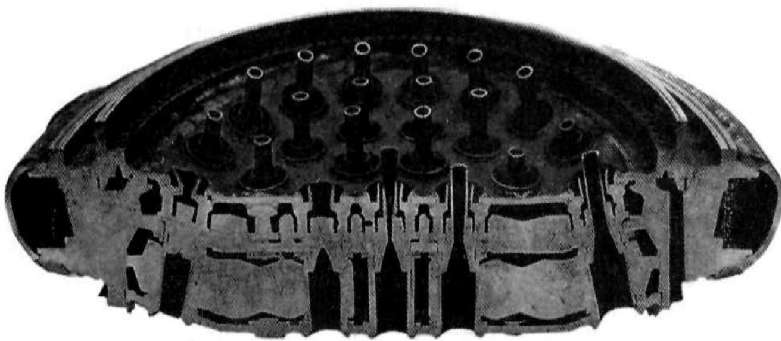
Сферическая форсуночная головка ЖРД со струйно-центробежными форсунками
